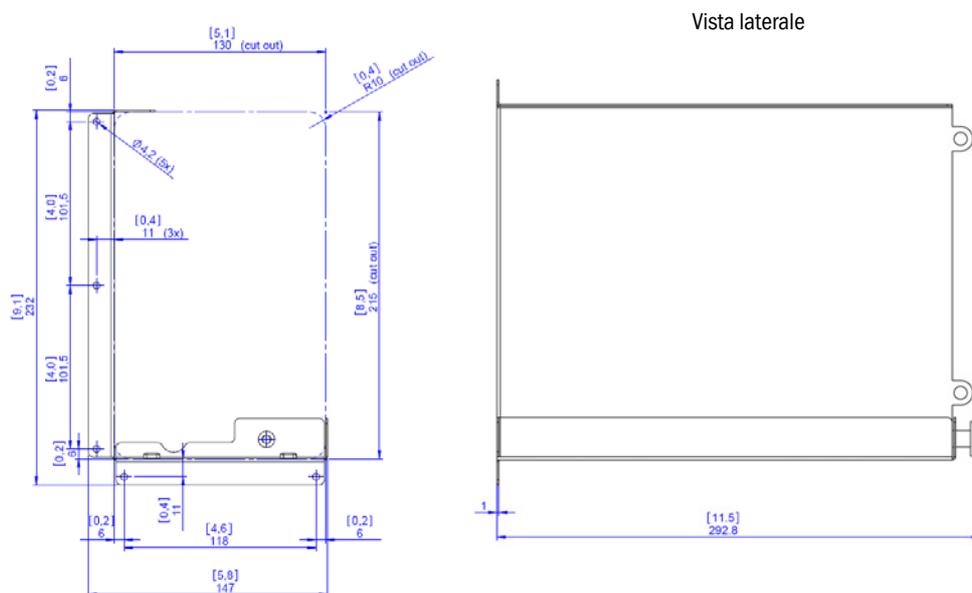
Dimensioni della staffa per montaggio a parete del Flow-X/C
